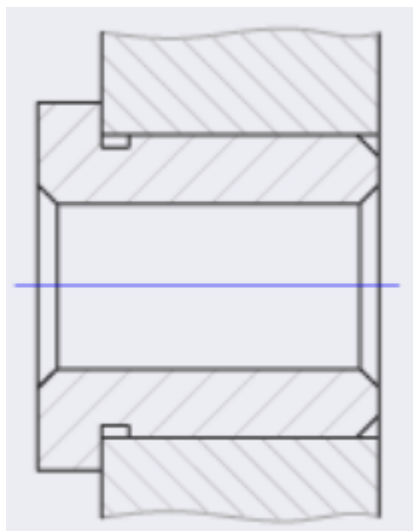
Креслення нероз'ємного нерегульованого підшипника ковзання
